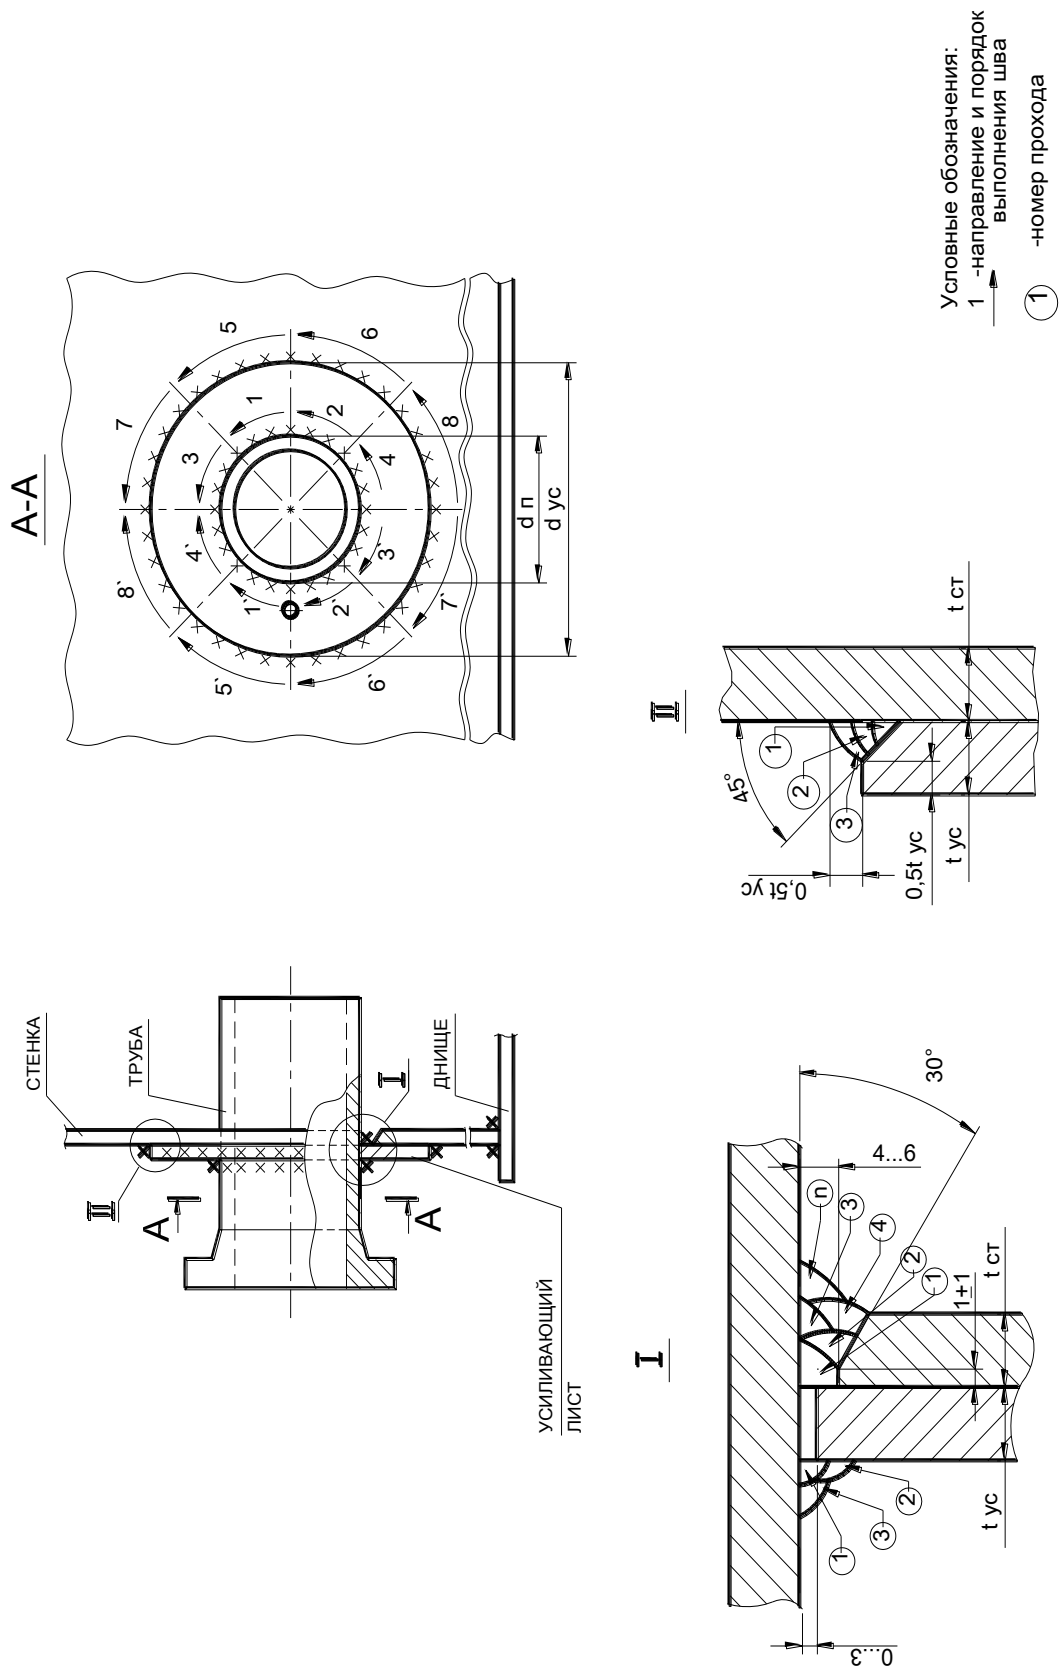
Схема сварки патрубков в стенке с усиливающим листом
